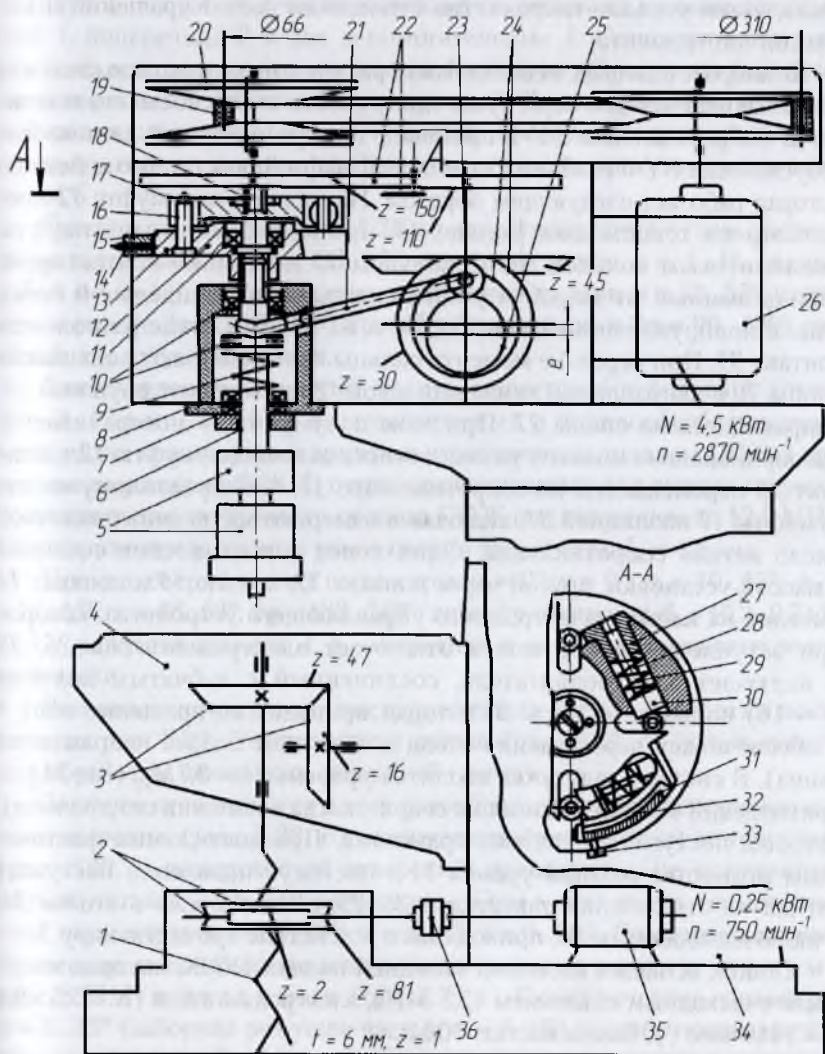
Устройство модернизированного вертикально-сверлильного станка мод. 2Н135-1 (виброустановка ВУ-6)
